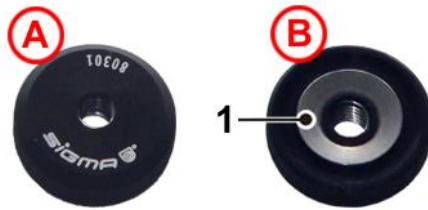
Écrou de fixation du rotor vu de dessus (A) et de dessous (B)
